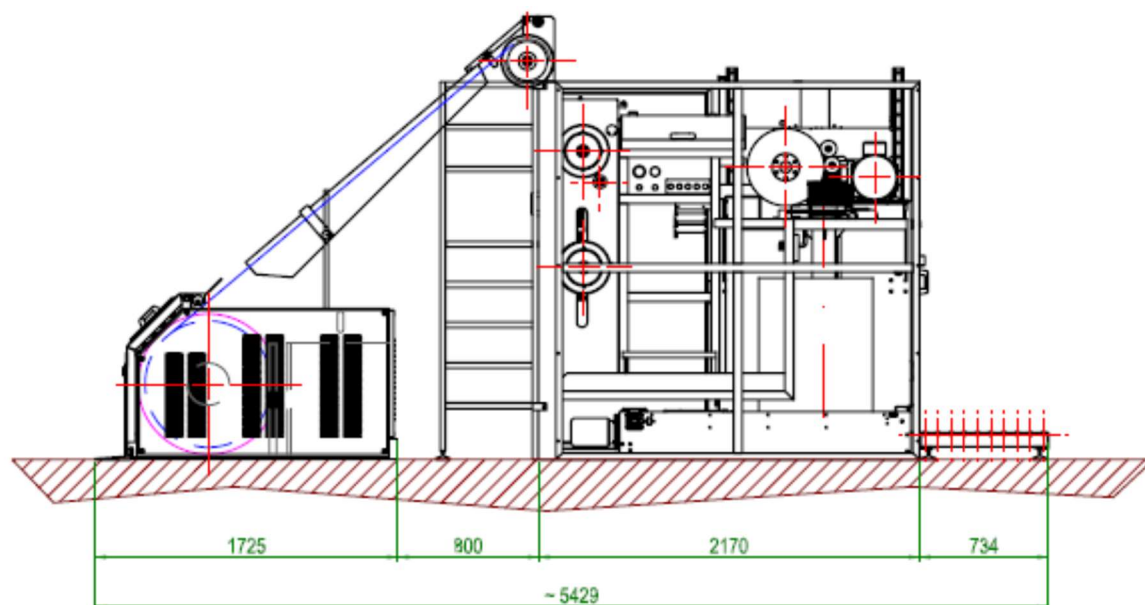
Layout da linha INF-4. Dimensões de instalação com desbobinador padrão e posicionamento dos acessórios elétrico e pneumático.
